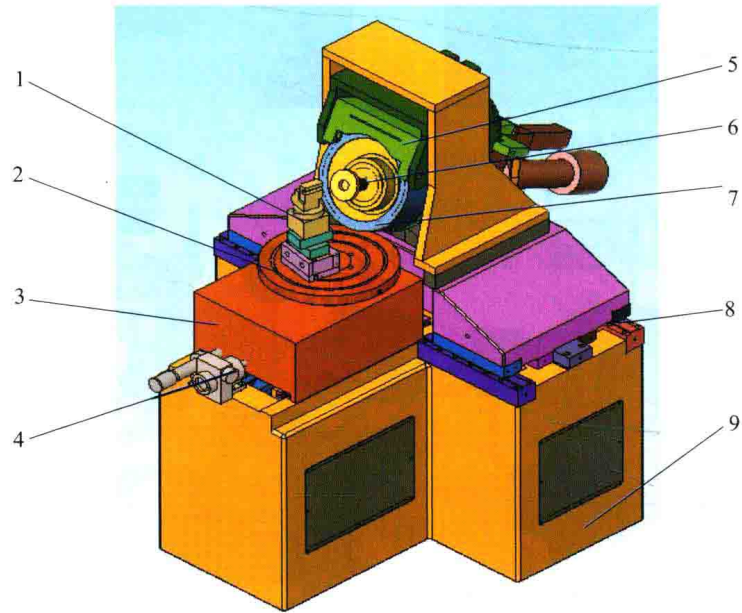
圆弧刃金刚石刀具刃磨机总体结构
